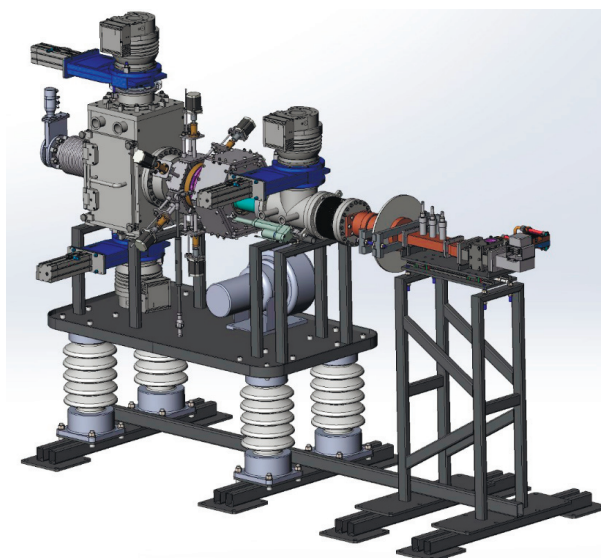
Общий вид конструкции ЭЦР ионного источника
